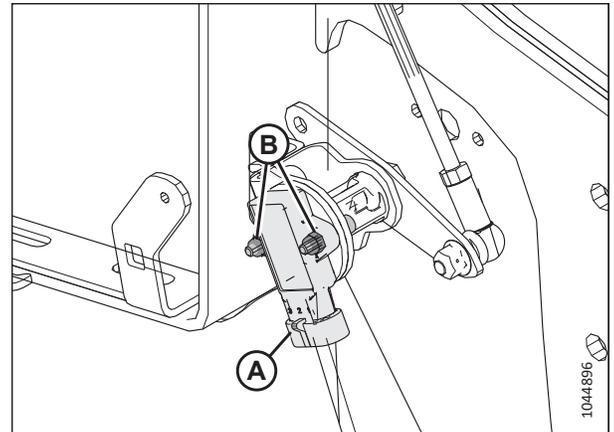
Haspelhöhsensor – Rechter Haspelarm
